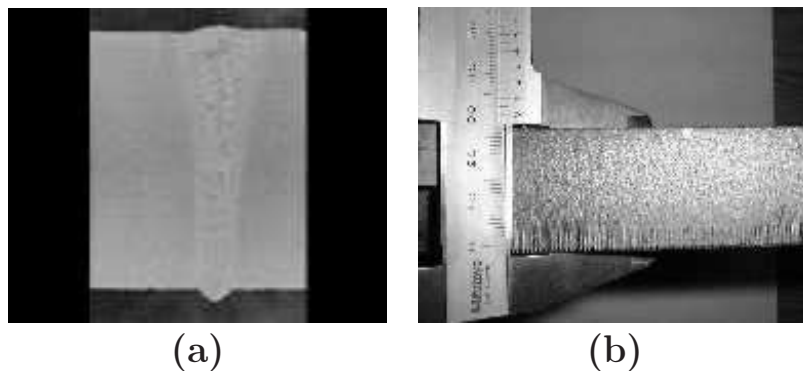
(a) Soudure de deux pièces d'acier de 12 mm d'épaisseur avec un laser  $\text{CO}_2$  [9]. (b) Découpe d'une plaque d'acier de 30 mm d'épaisseur à l'aide d'un laser  $\text{CO}_2$  [10].
